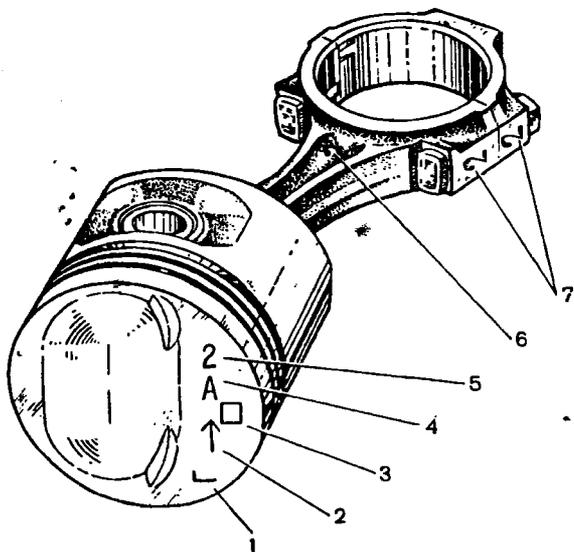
Маркировка поршня и шатуна: 1 - группа поршня по массе; 2 - стрелка для ориентирования поршня в цилиндре; 3 - ремонтный размер; 4 - класс поршня; 5 - класс отверстия для поршневого пальца; 6 - отверстие для выхода масла; 7 - номер цилиндра
